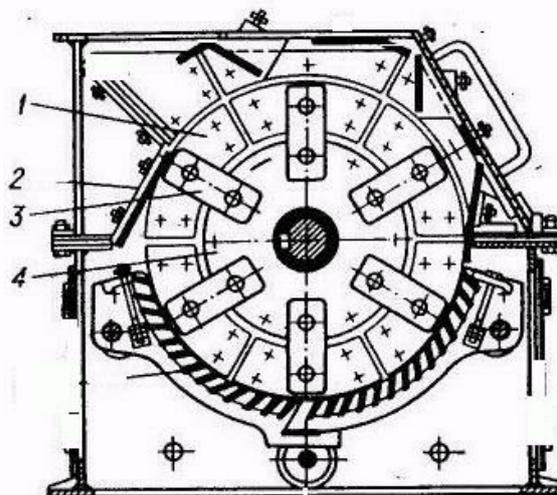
Однороторная молотковая дробилка: 1 – крепление; 2 – корпус; 3 – молотки; 4 – ротор
